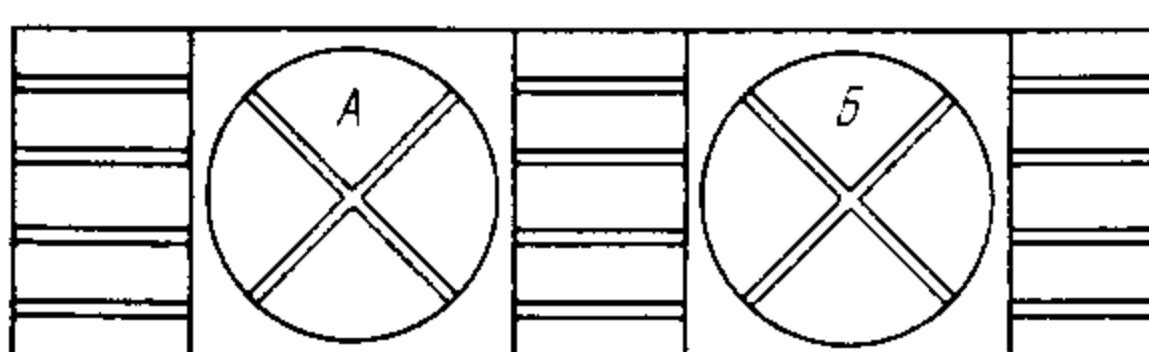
Прямоугольный стол с двумя встроенными поворотными столами
